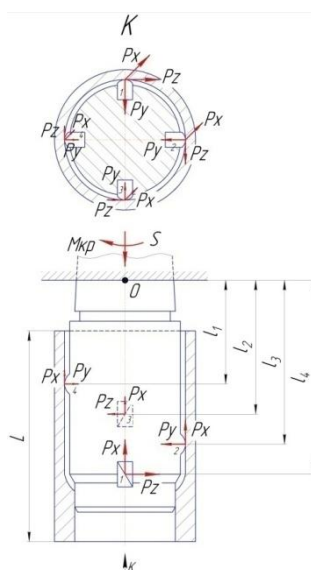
Действующие силы на сборную резцовую развёртку
